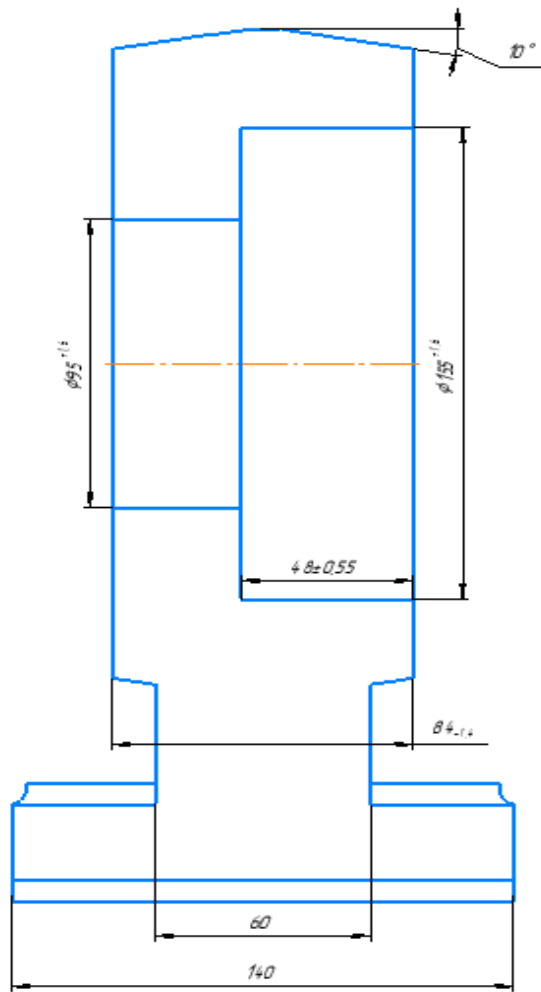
Эскиз детали «Корпус подшипника»
